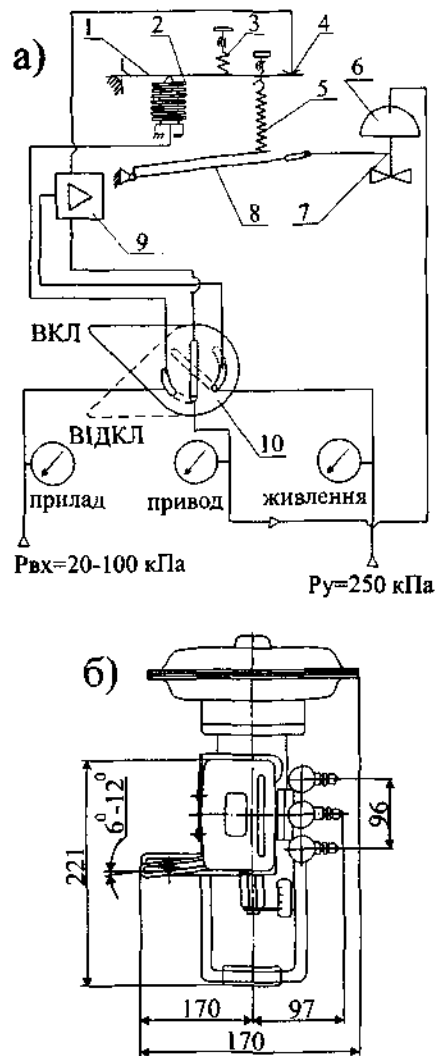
Пневматичний позиціонер типу ППС-100: а-принципова схема; б-монтаж позиціонера на механізмі типу МИМ ОПХ-250.
